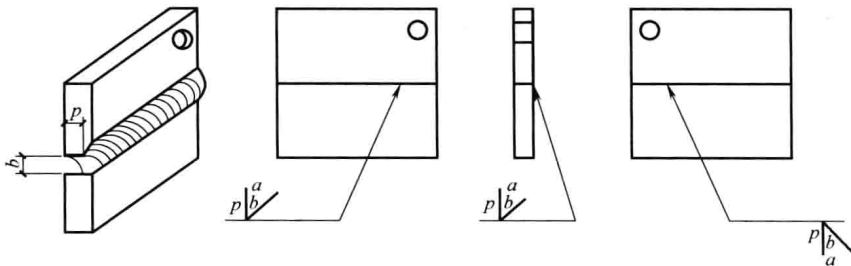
1个焊件带坡口的焊缝标注方法
